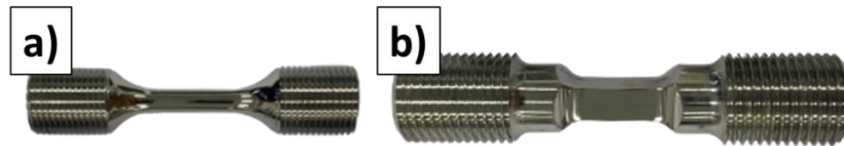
Images des éprouvettes après usinage. a) Eprouvette cylindrique. b) Eprouvette à section carrée.
